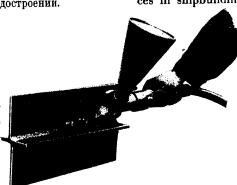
Держатель ДПП-5 при сварке стыкового шва
